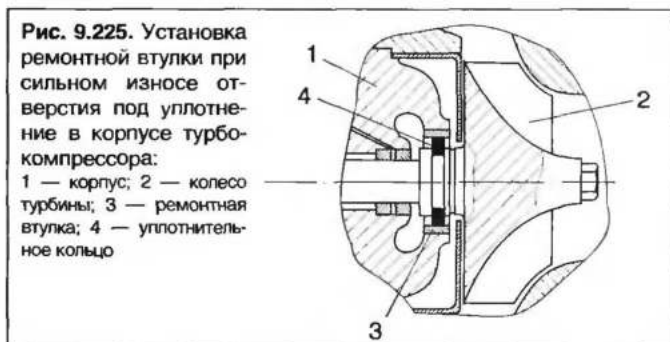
Установка ремонтной втулки при сильном износе отверстия под уплотнение в корпусе турбокомпрессора:
